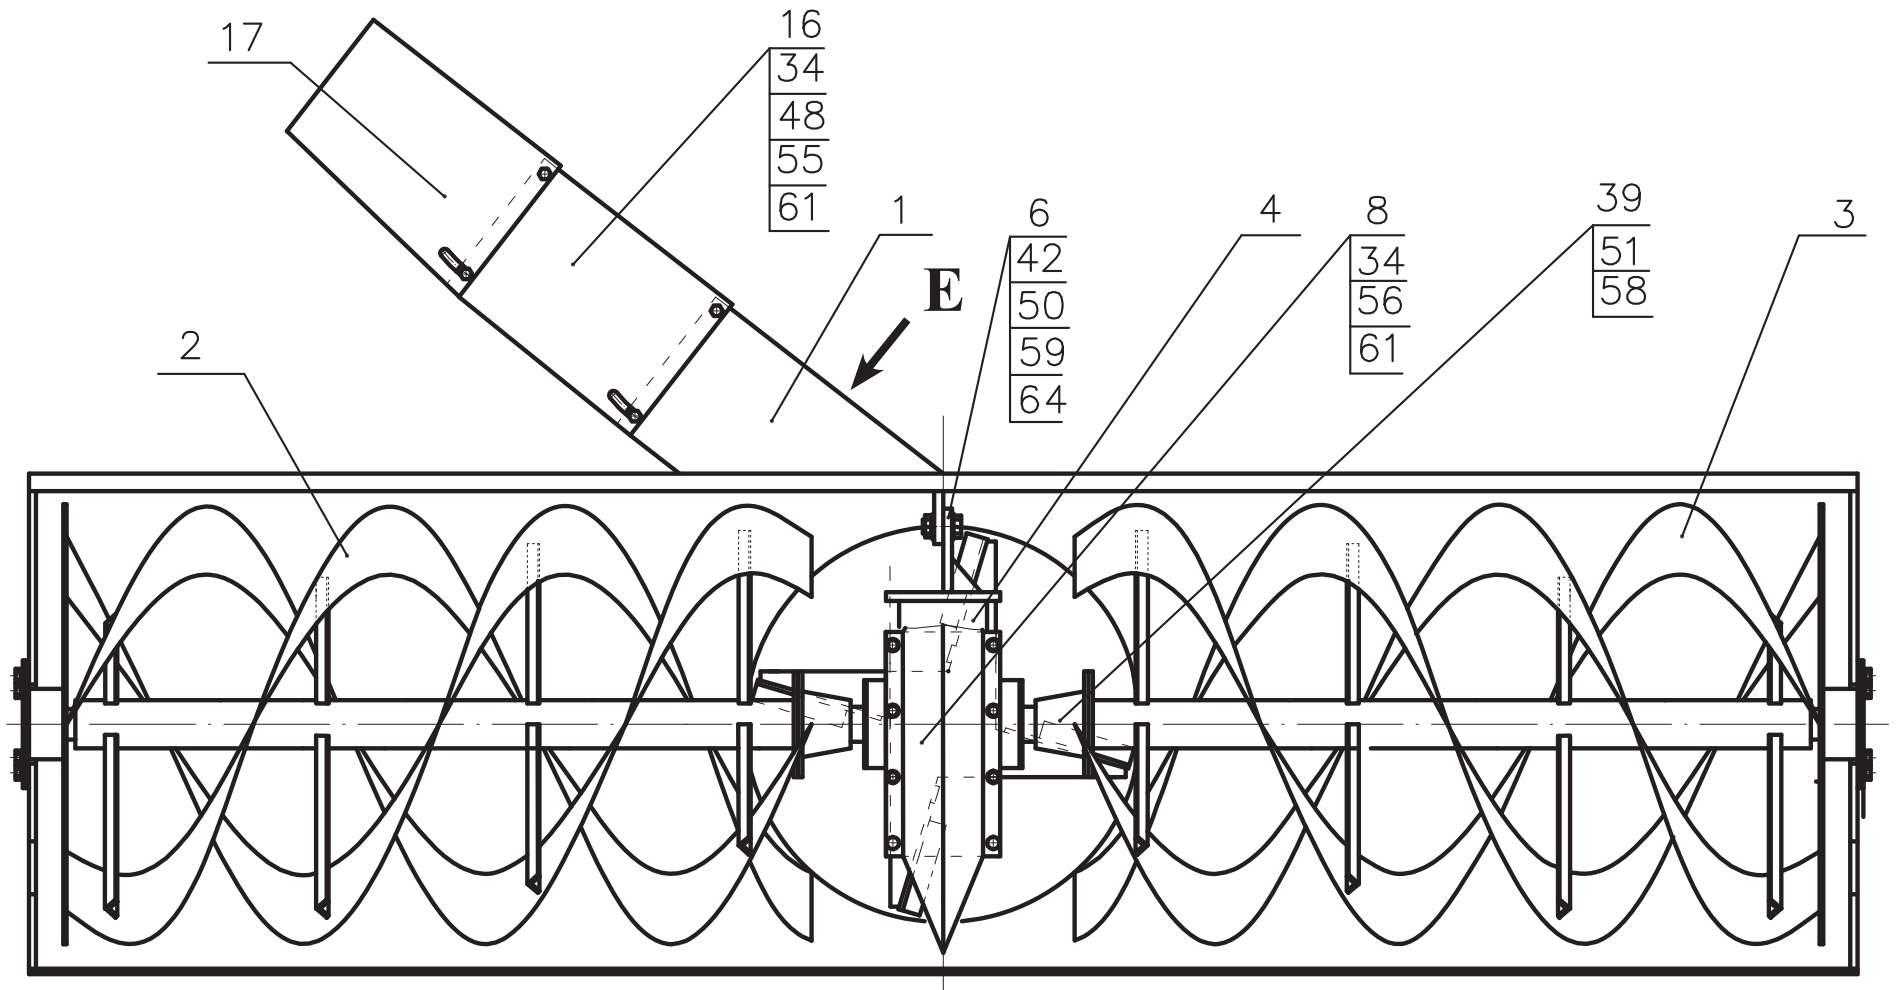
208.46.55.000	Снегоочиститель фрезерно-роторный
